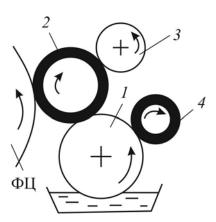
Увлажняющий аппарат для подачи спиртового раствора: I — дукторный цилиндр; 2 — накатной валик; 3 — раскатной цилиндр; 4 — отжимной валик; Φ Ц — формный цилиндр
